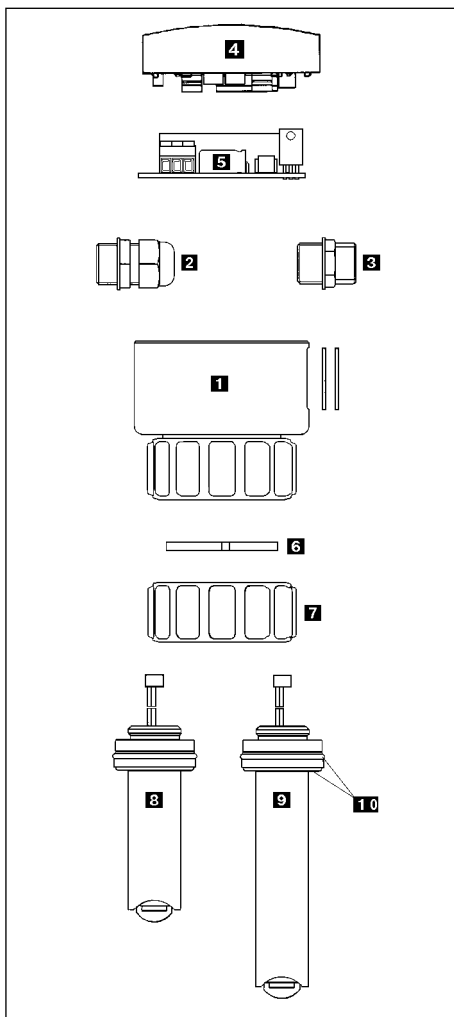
Ersatzteil Explosionszeichnung kompakte Ausführung
